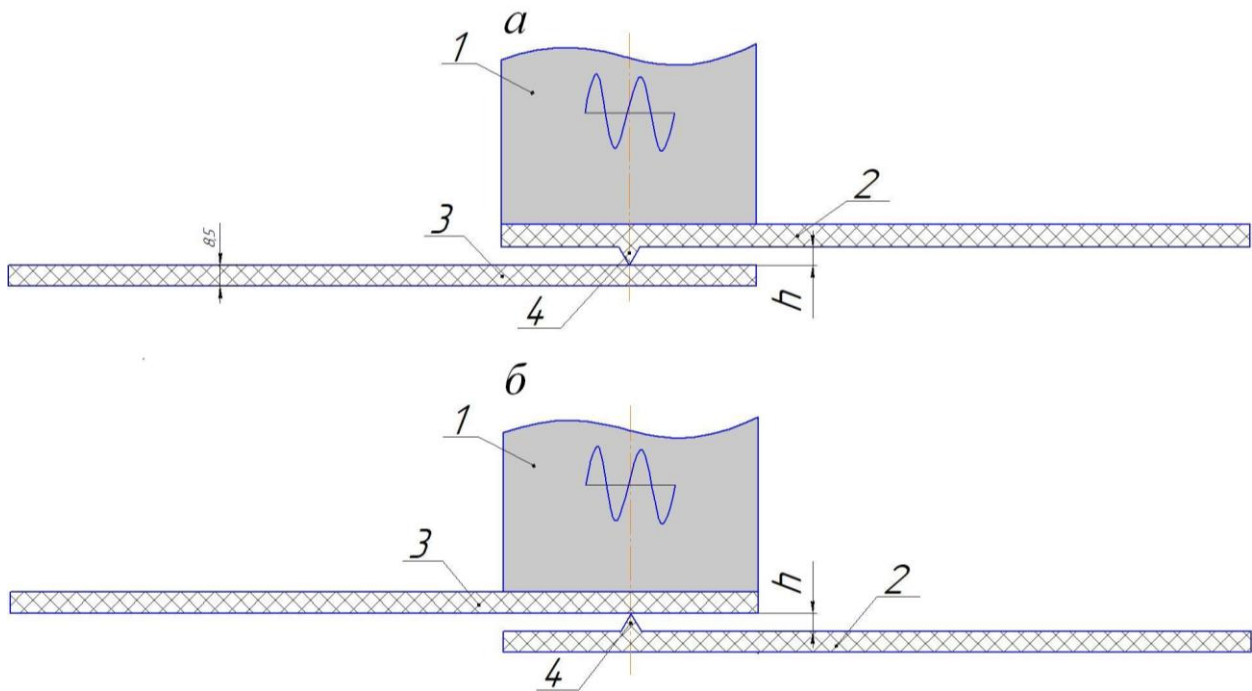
Схема ультразвуковой сварки образцов с различным расположением концентратора энергии: (а) подача ультразвуковой энергии сверху, (б) подача ультразвуковой энергии снизу: 1 – излучатель, 2 – образец с концентратором энергии, 3 – образец без концентратора энергии, 4 – концентратор энергии, h – высота концентратора энергии
